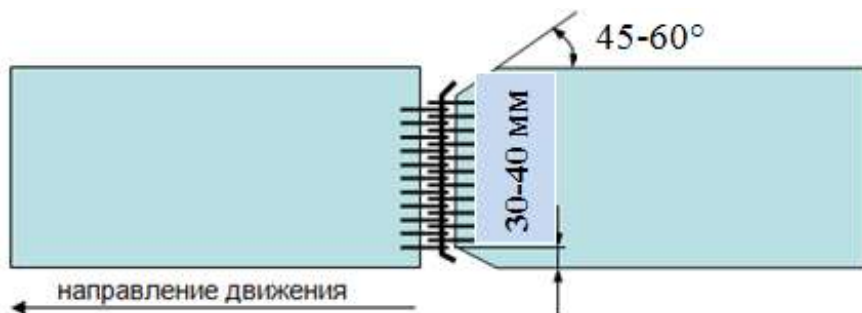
Установка соединительного стержня и заделка ведомого конца ленты
